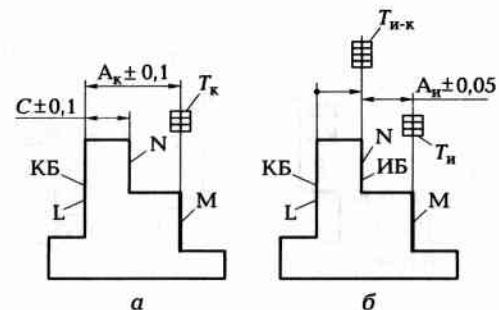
Несовмещение исходной базы и конструкторской базы (ИБ \neq КБ)
